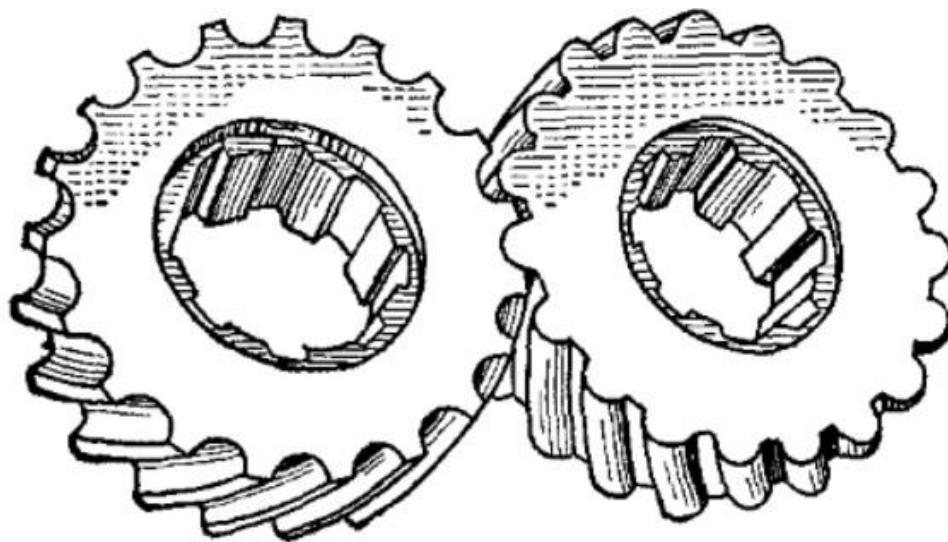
Цилиндрическая зубчатая передача Новикова
